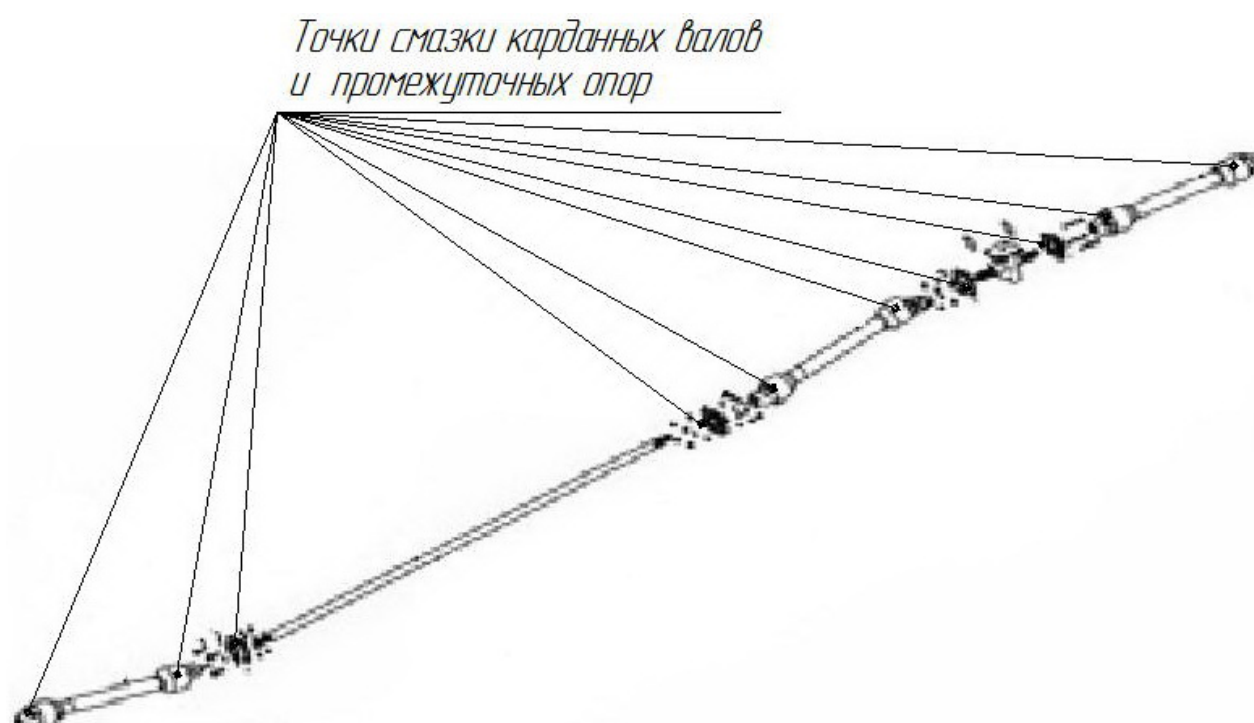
Смазка шлицевых соединений, крестовин карданных валов и подшипников промежуточных опор
